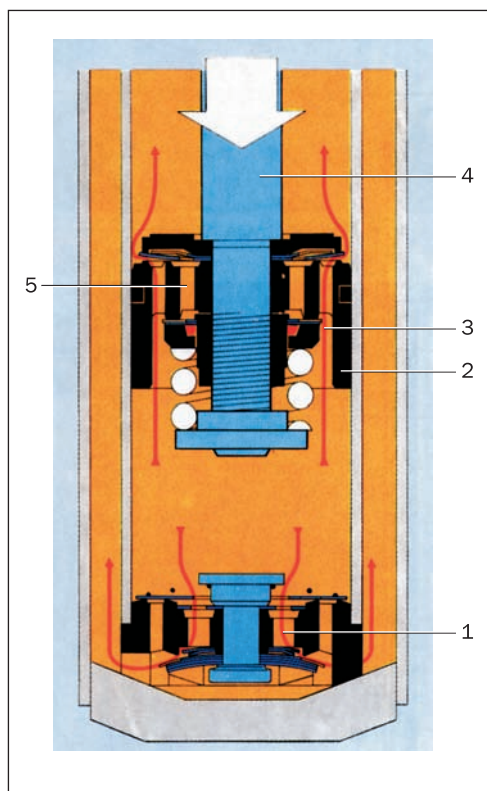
Схема работы двухтрубного амортизатора: 1 — донный клапан; 2 — поршень; 3 — клапан сжатия; 4 — шток; 5 — клапан отбоя
